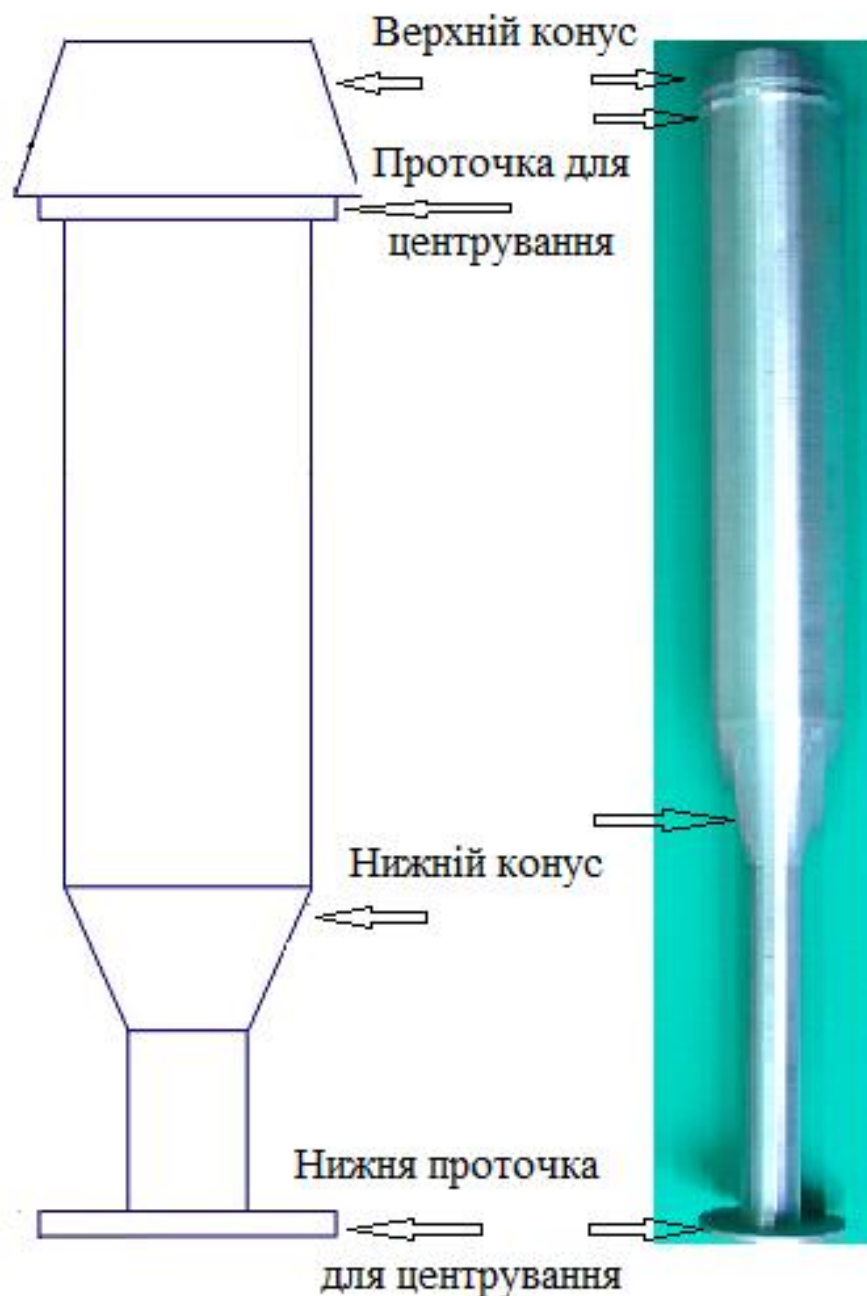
Схема алюмінієвої заготовки спеціальної форми і заготовка після токарного оброблення
